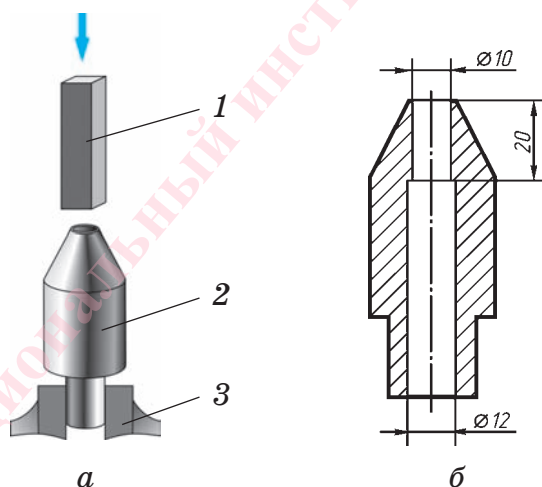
Технический рисунок (а) и чертеж (б) приспособления для изготовления деталей с цилиндрической поверхностью $\varnothing 10$ мм:
